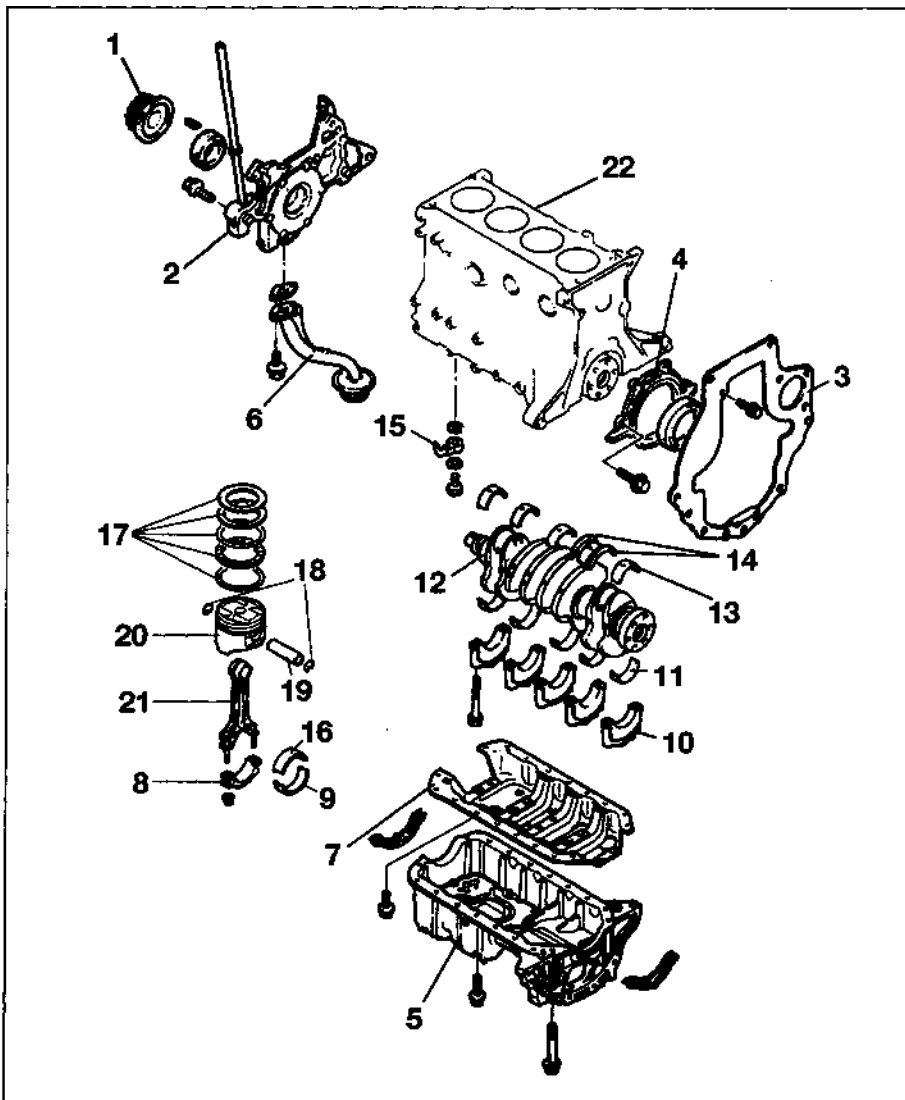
Узлы и детали нижней части 4-цилиндрового двигателя
